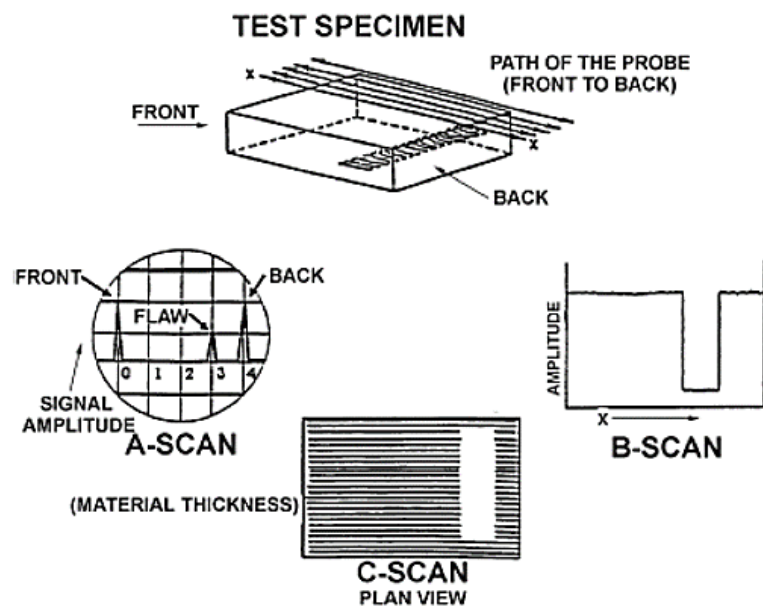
Esquemas A-scan, B-scan, C-scan. Fuente [17]
